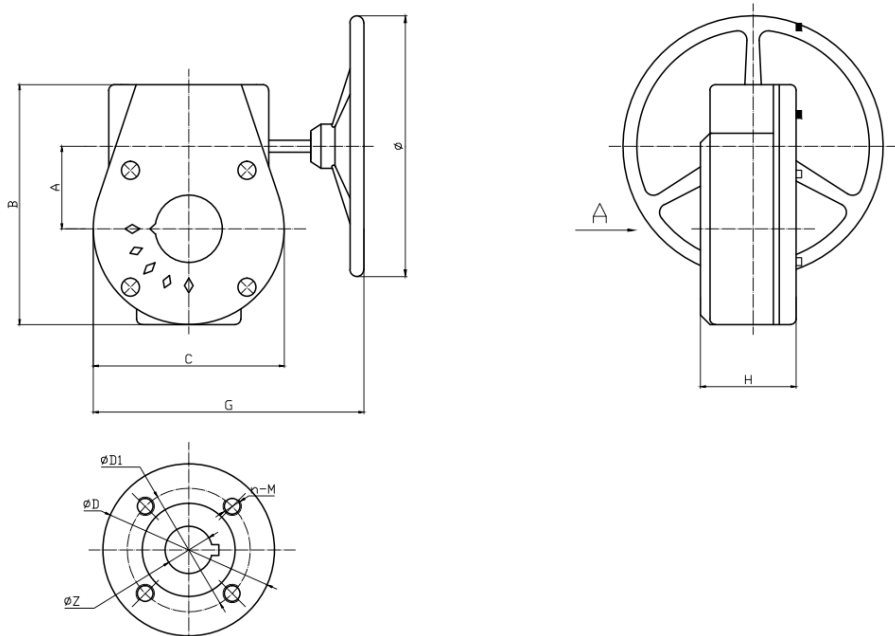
Габаритные размеры редукторов типоразмеров А-I – А-IV DN50-DN450.
